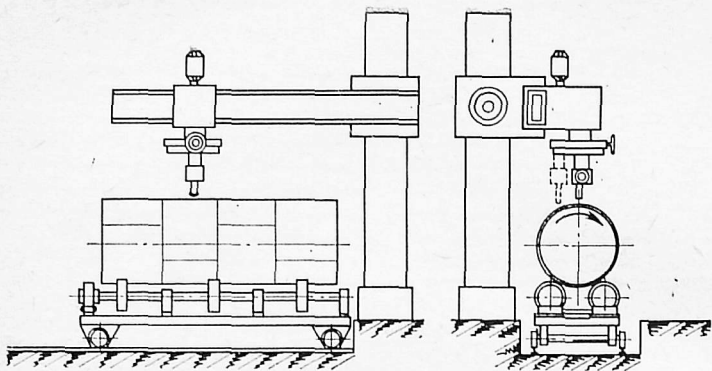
Схема универсальной сварочной установки для сварки крупных узлов.
